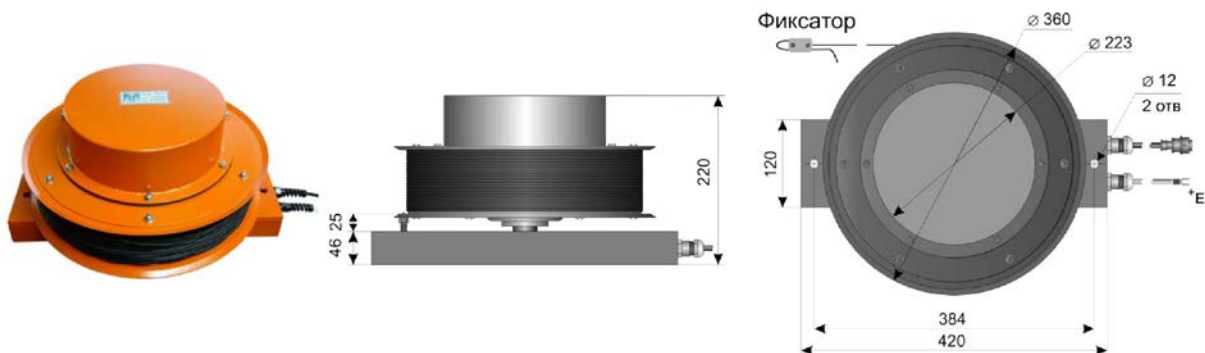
Внешний вид и габариты датчика длины стрелы АС-ДДЛ-02.2+
